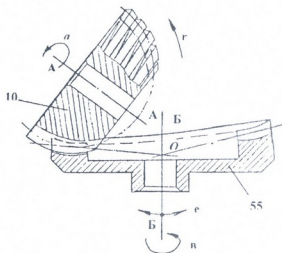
Схема нарезания конического колеса с наружными зубьями
